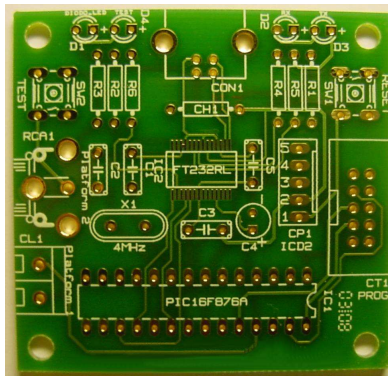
FOTO DE UMA PLACA DE CIRCUITO IMPRESSO NÃO MONTADA.
